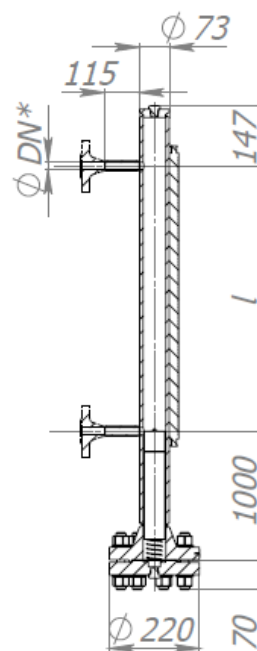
Габаритные и присоединительные размеры указателя уровня дапасного SIRIUS 16 МПа
